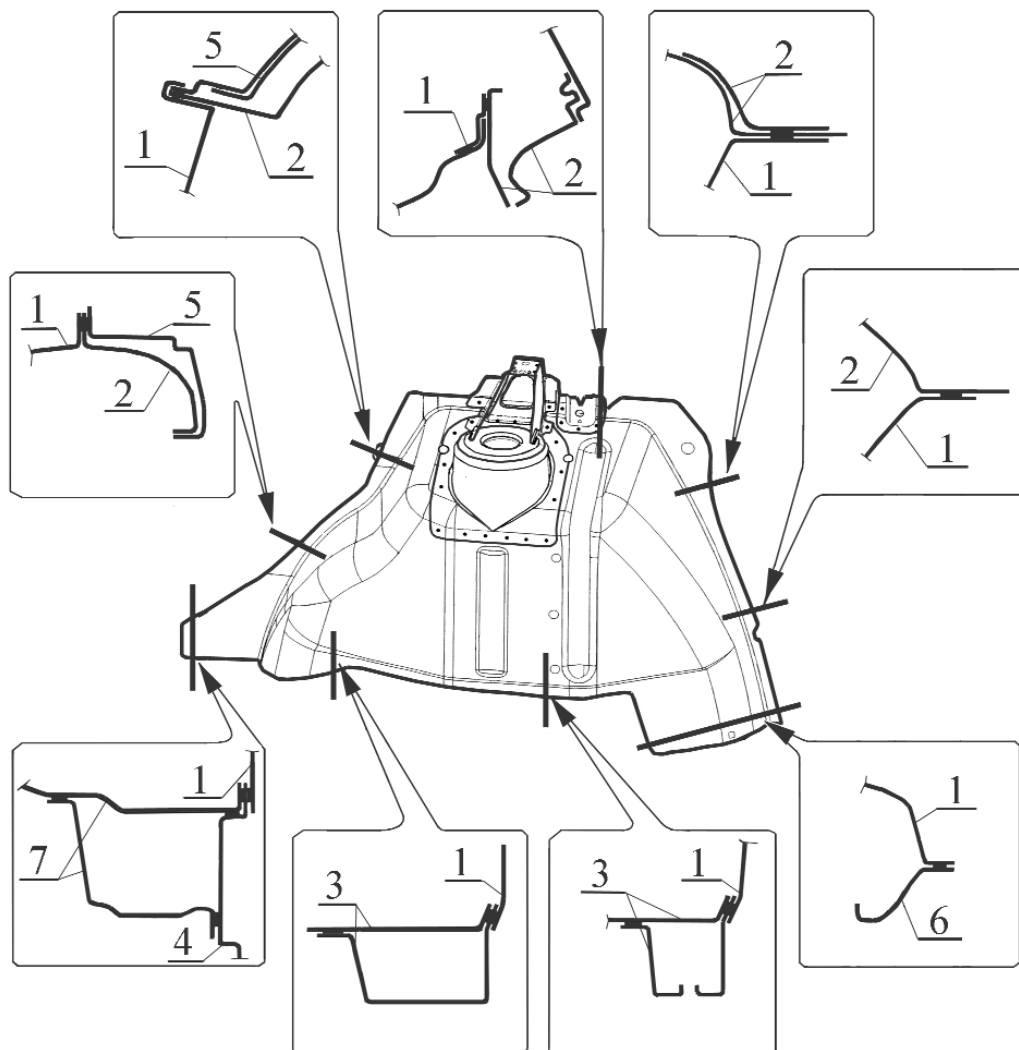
Соединение арки заднего колеса в сборе с сопрягаемыми деталями.
